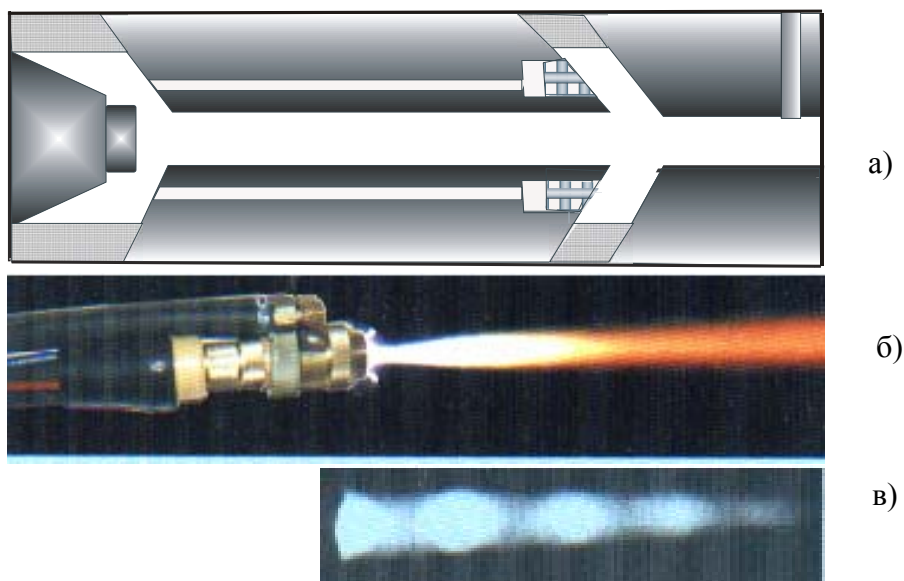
Сверхзвуковой плазмотрон для напыления покрытий
